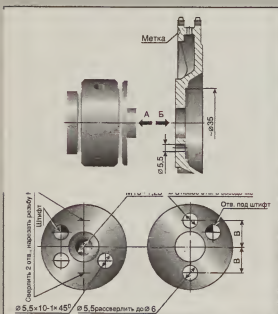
Ремонт (с доработкой) торца распределительного вала (вид А) и звездочки (вид Б).
